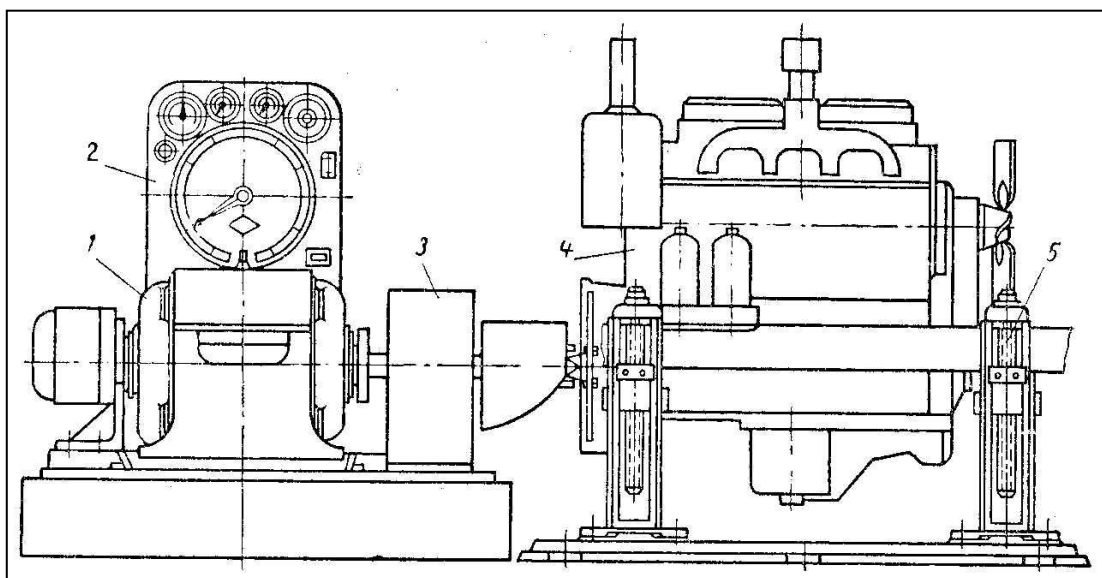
Схема расположения малогабаритных стендов для обкатки автомобильных двигателей
